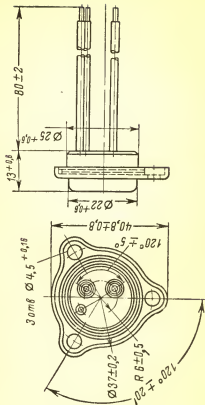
Габаритный чертеж диодов Д238А—Д238Е.
